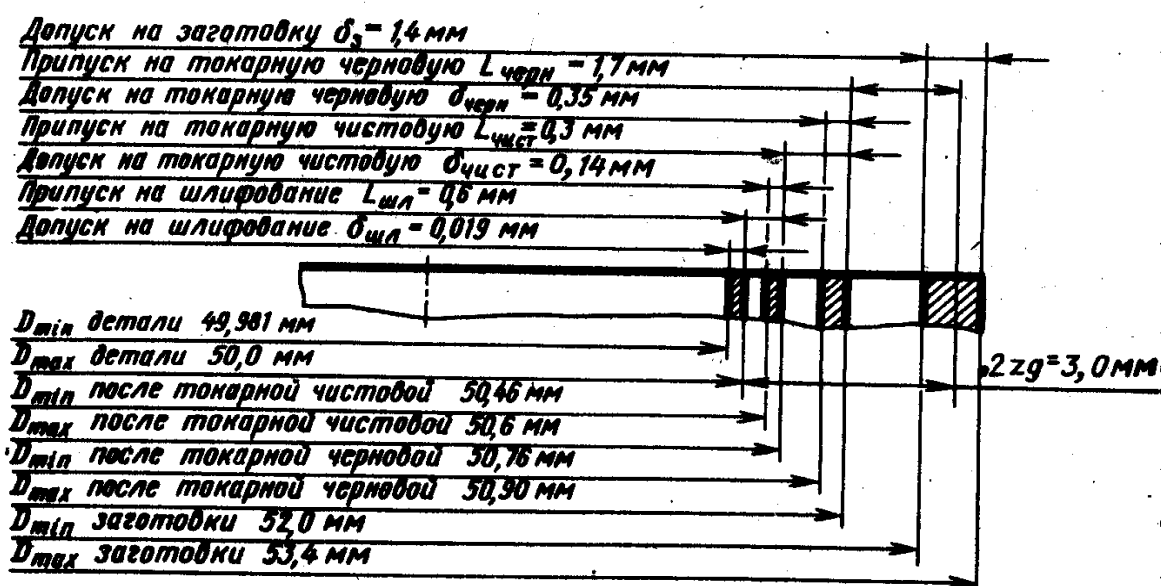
Пример расположения полей допусков и промежуточных размеров для операций
